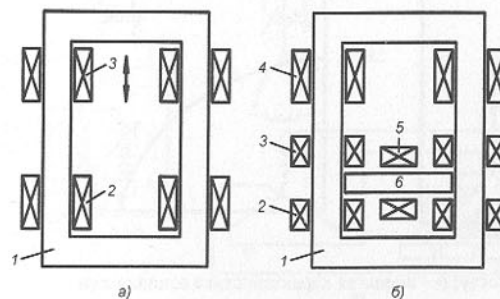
Схемы сварочных трансформаторов
